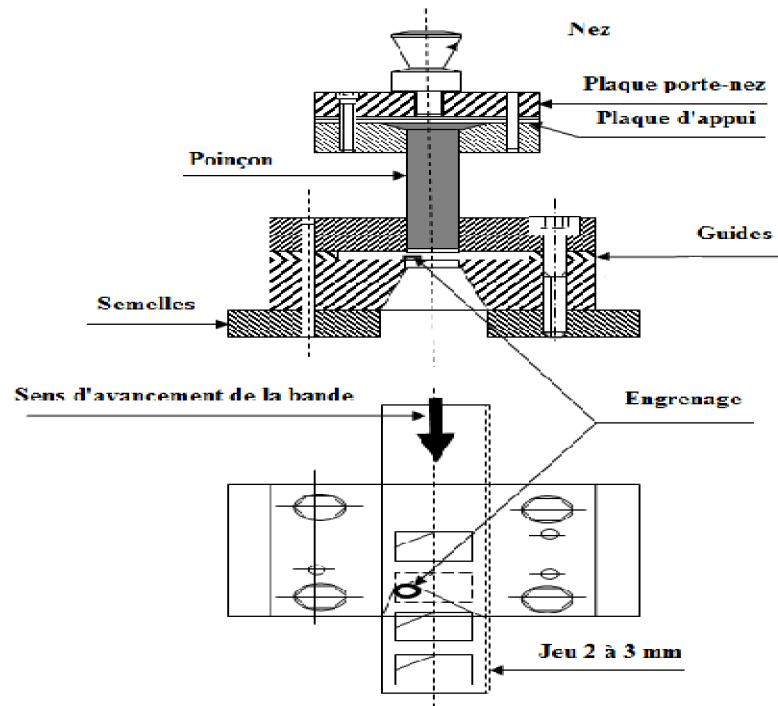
Principe de l'Outil à Contre-plaque à Engrenage.
